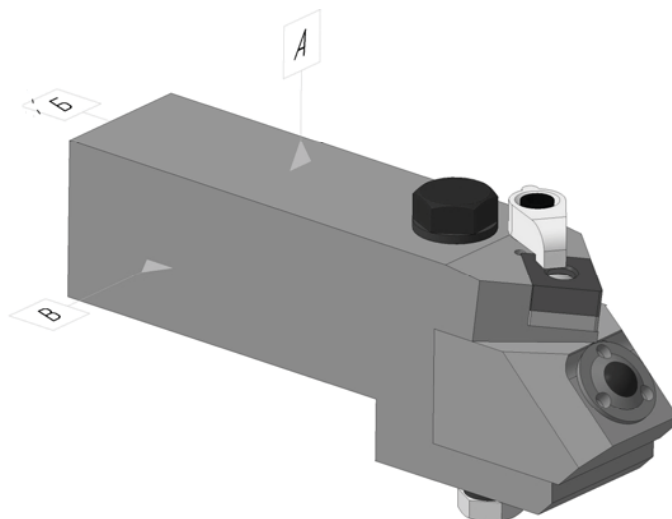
Инструмент для совмещенной обработки деталей точением и накатыванием с гидроприводом
